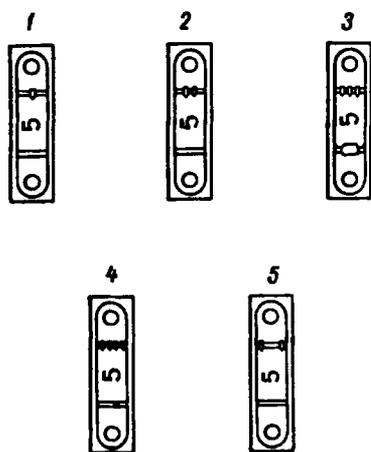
Метки на крышках коренных подшипников (счет опор ведется от передней части двигателя) и условный номер блока цилиндров
